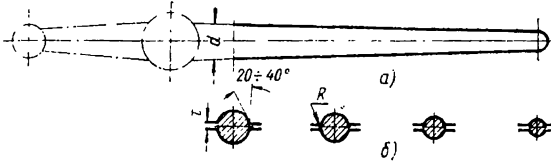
Конусный участок заготовки (а), полученный одноручьева вальцовкой в открытом ручье (б)
